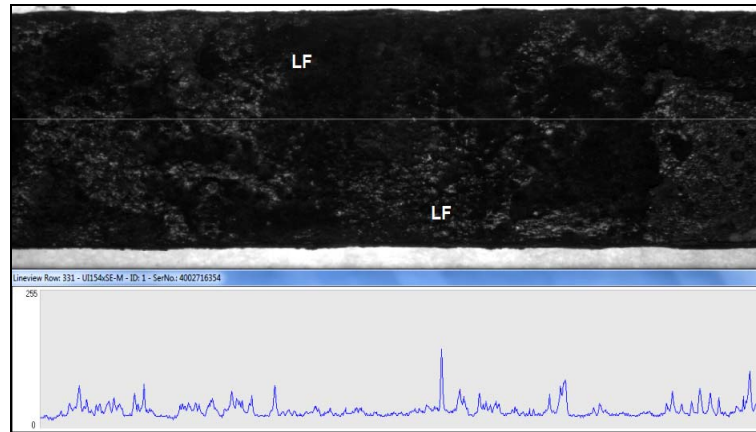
Superficie de la probeta con soldadura SMAW a compresión.
